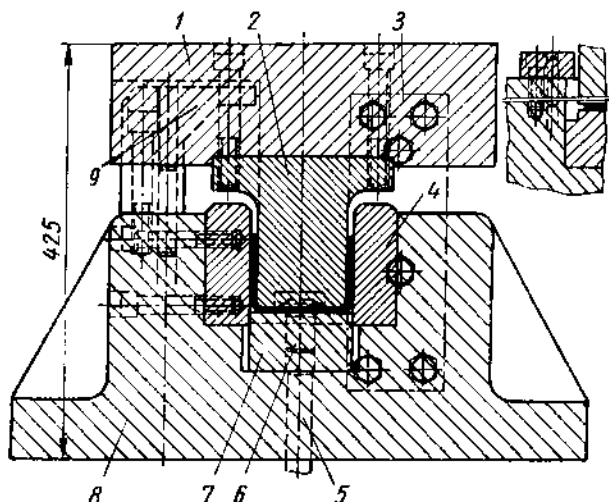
Двухугольный гибочный штамп с прижимом материала для штамповки поперечины рессор грузового автомобиля
